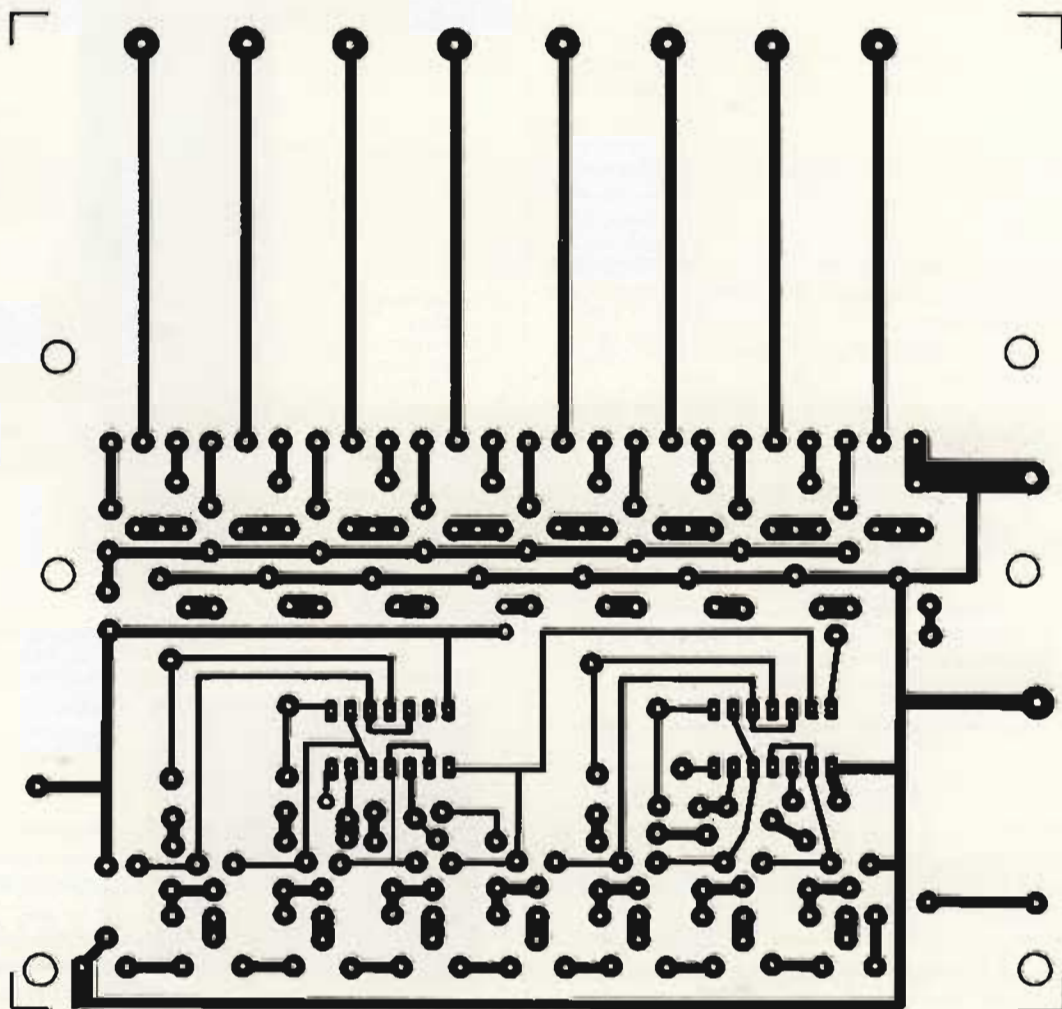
a - Circuito stampato della basetta II (lato saldature) - Scala 1:1.
